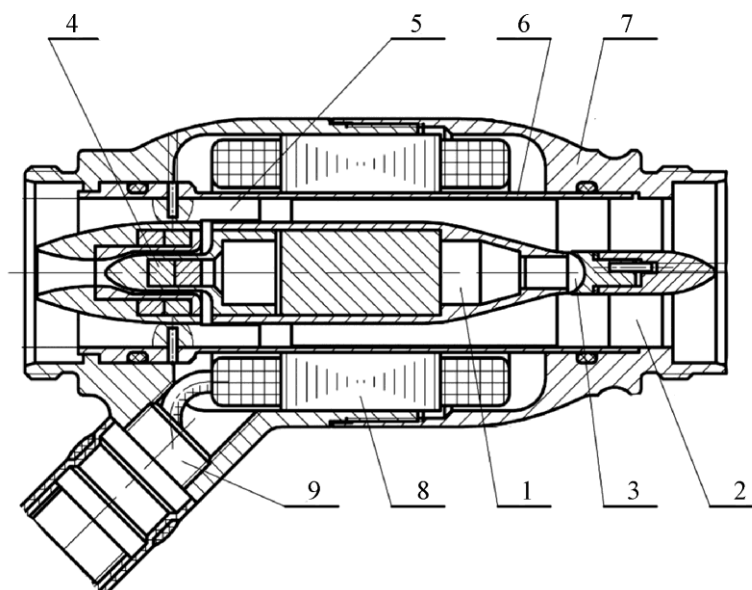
Конструкция насоса: 1 – ротор насоса; 2 – направляющий аппарат; 3 – опора скольжения ротора; 4 – магнитный подвес ротора; 5 – спрямляющий аппарат; 6 – изолирующая втулка; 7 – корпус насоса; 8 – статор электрической машины; 9 – узел ввода кабеля питания и управления
